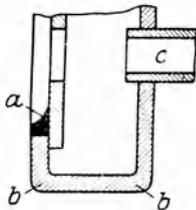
Unterer Teil einer neueren Ausführung der Wasserkammer. Die älteren Wasserkammern haben bei b Schweißstellen, die schwierig auszuführen waren und durch Aufreißen zu Kesselexplosionen Anlaß gaben. Die Schweißstelle a der neueren Wasserkammern ist sicherer herzustellen, c = die unterste Reihe der Siederohre.
